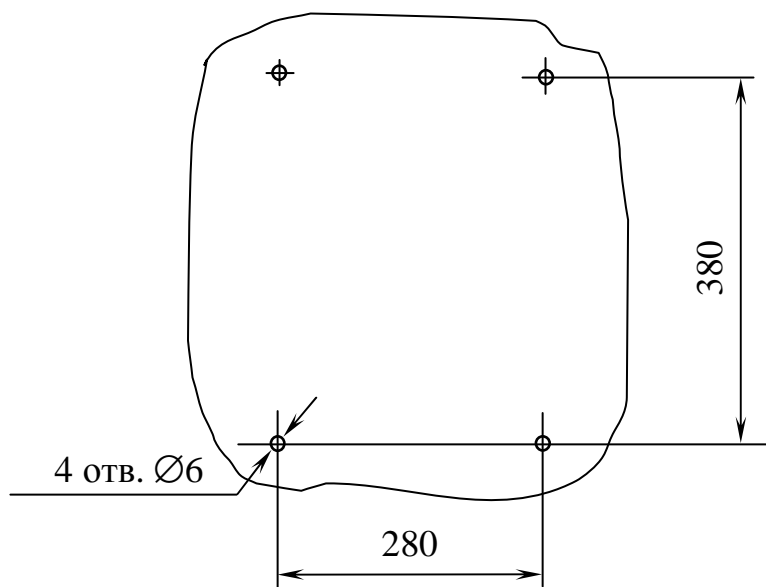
Расположение отверстий для крепления гидропанели ГП-1002
